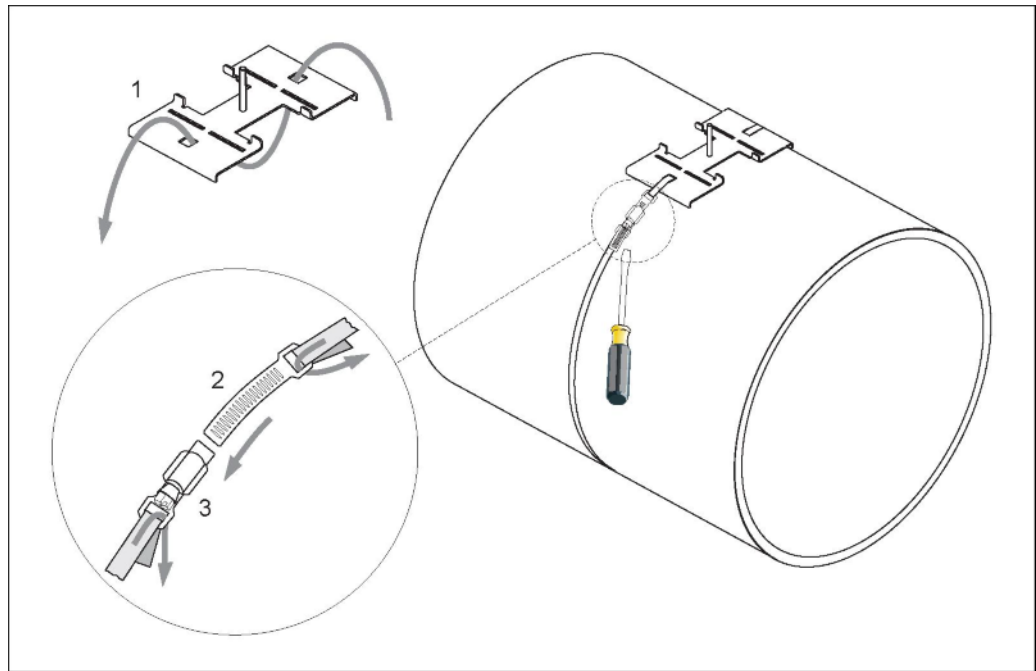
Предварительный монтаж крепежных лент для трубопроводов диаметром DN > 200
